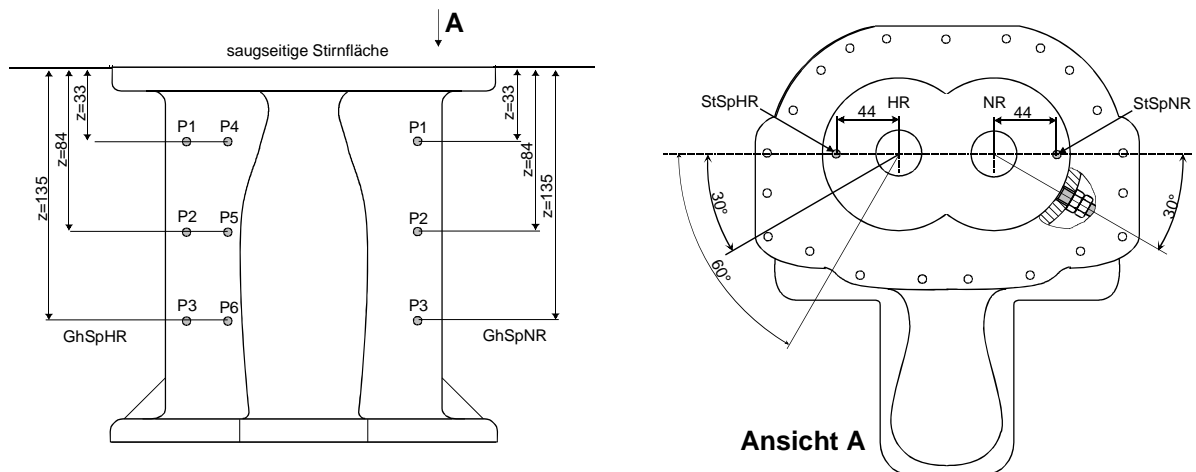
Positionen der Wegmessaufnahme im Rotorgehäuse /1/
